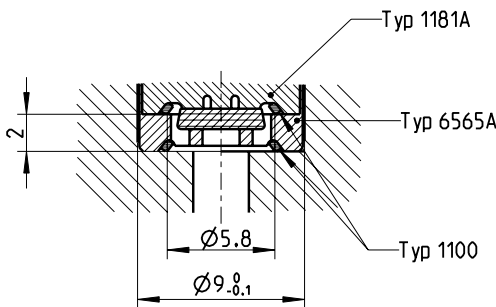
Einbau mit Thermoschutzplatte (Typ 1181A) und Thermoschutzschild (Typ 6565A)
